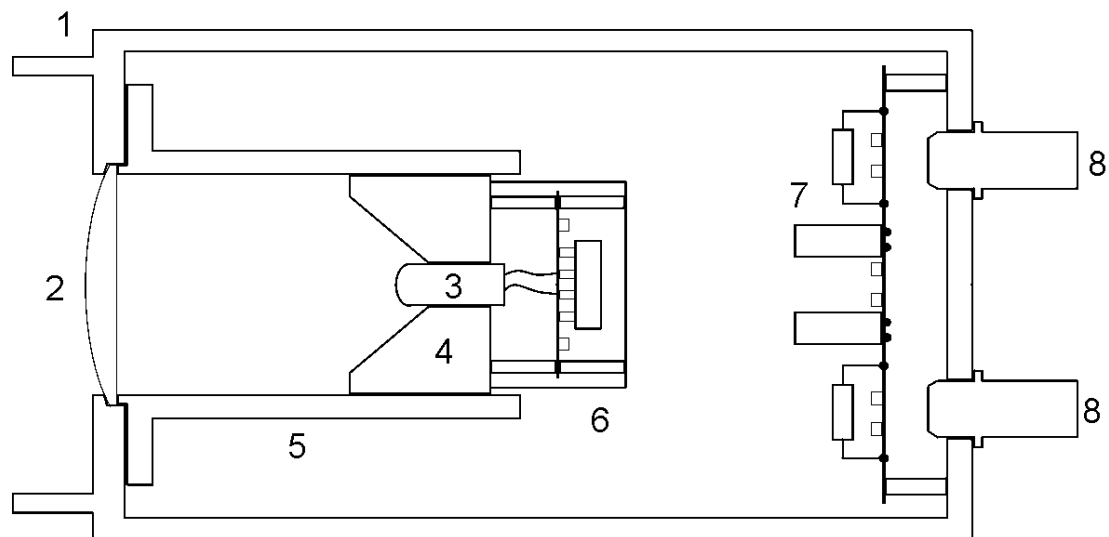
Конструкция фотометрической головки: 1 – корпус, 2 – линза, 3 – фотодиод, 4 – держатель фотодиода, 5 – тубус держателя фотодиода, 6 – входной усилитель фототока, 7- плата фильтров питания, 8 – разъёмы
